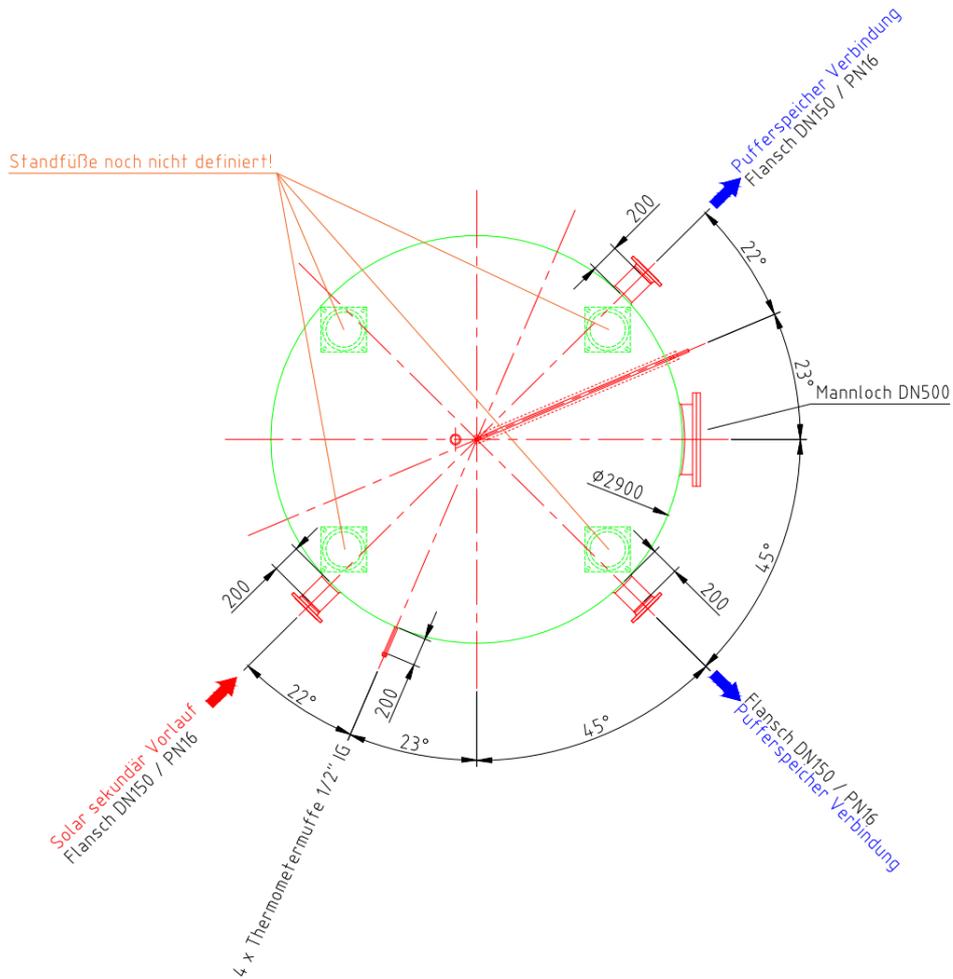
Pufferspeicher Grundriss, Variante 1
